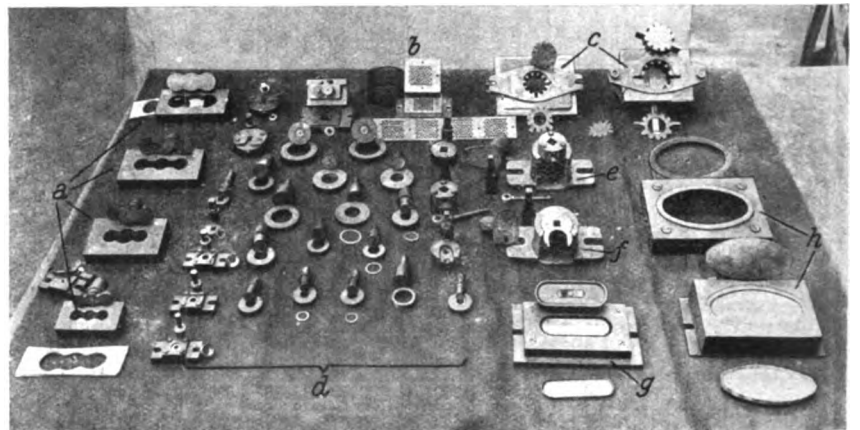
a) Schnittwerkzeuge für Stangenlagerschmiergefäßdichtungen, b) Vorrichtung zum Lochen von Luftsaugventilsieben, c) Schnitte zur Herstellung der Kolbenschiebersicherungen, d) Schnittzeuge zur Fertigung von Dichtungen, Scheiben u. dergl., e) Werkzeug zum Lochen der vorgebohrten Hahngriffe, f) desgl. für Lappenbolzen, g) vereinigt Schnitt- und Stanzzeug für Achslagerschmierdeckel, h) Schnitt- und Stanzzeug für die Böden der Wasserkastenschwimmer.
